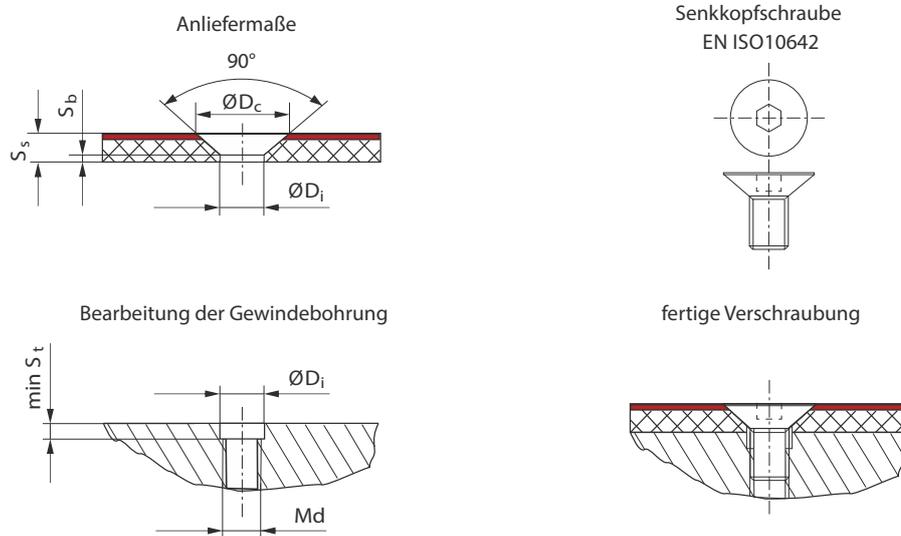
Gleitplattenbefestigung mit Senkkopfschrauben
